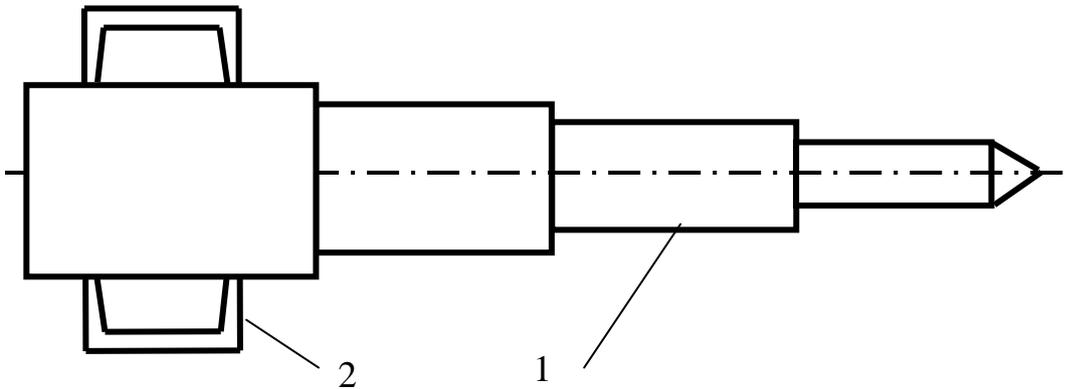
Схема установки зуба: 1 – палец зуб; 2 – швеллер (№27)
